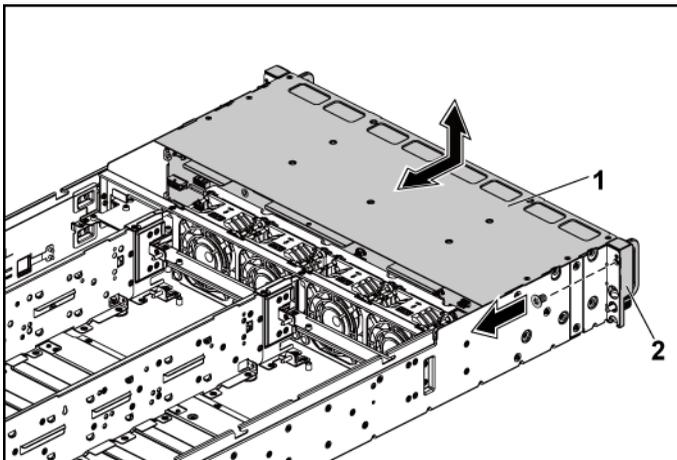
Rückwandplatine entfernen und installieren
